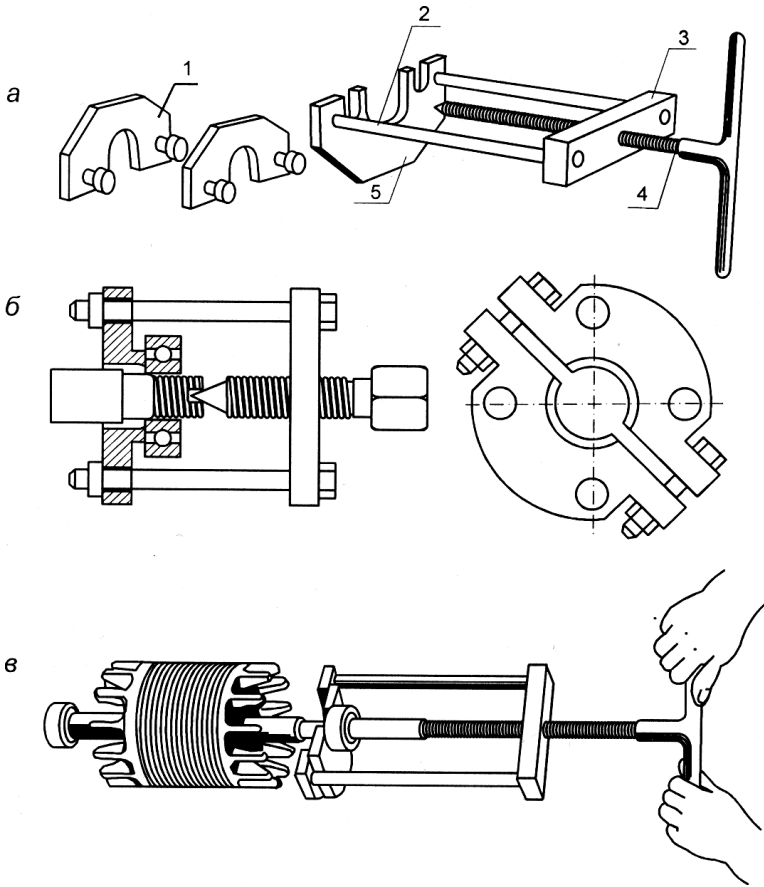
Съемники для съема подшипников с вала электродвигателя: *а* — универсальный съемник со сменной вставкой: 1 — вставка; 2 — тяга; 3 — поперечина; 4 — ходовой винт с рукояткой; 5 — упорная планка; *б* — съемник с разъемным захватом; *в* — съем подшипника с вала универсальным съемником
